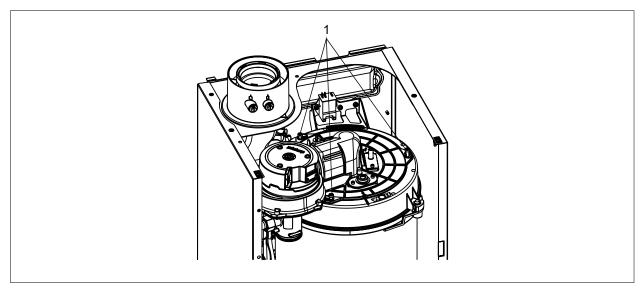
Desserrer la vis du couvercle de la chambre de combustion
